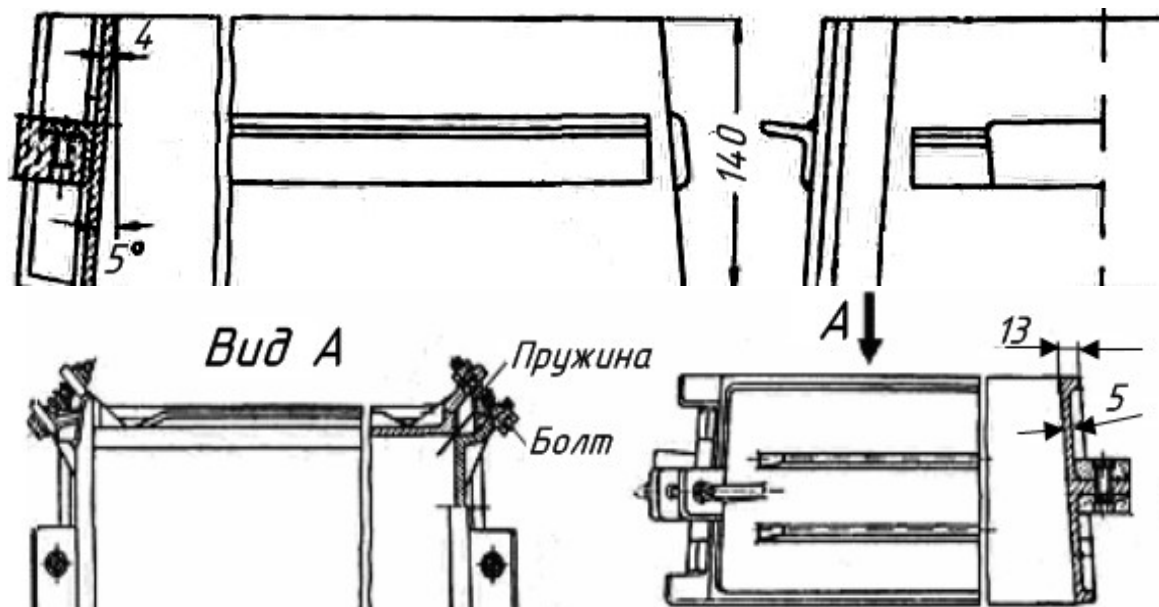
Жакеты: а – сварной жакет для безопочной формовки; б – пружинный жакет для безопочной формовки
